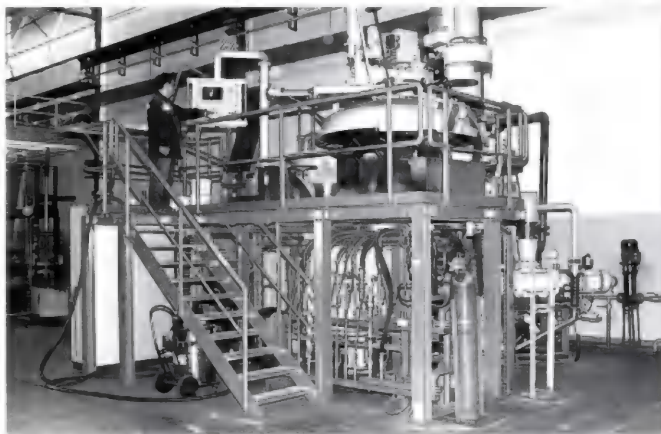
Установка по выплавке шихтовых заготовок жаропрочных сплавов для авиационных двигателей пятого поколения
